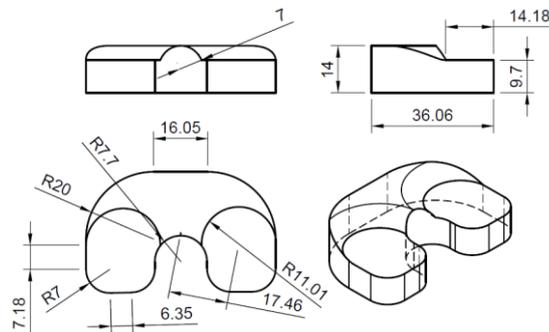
Pieza de componente inserto tibial hecha y acotada en Fusion 360
